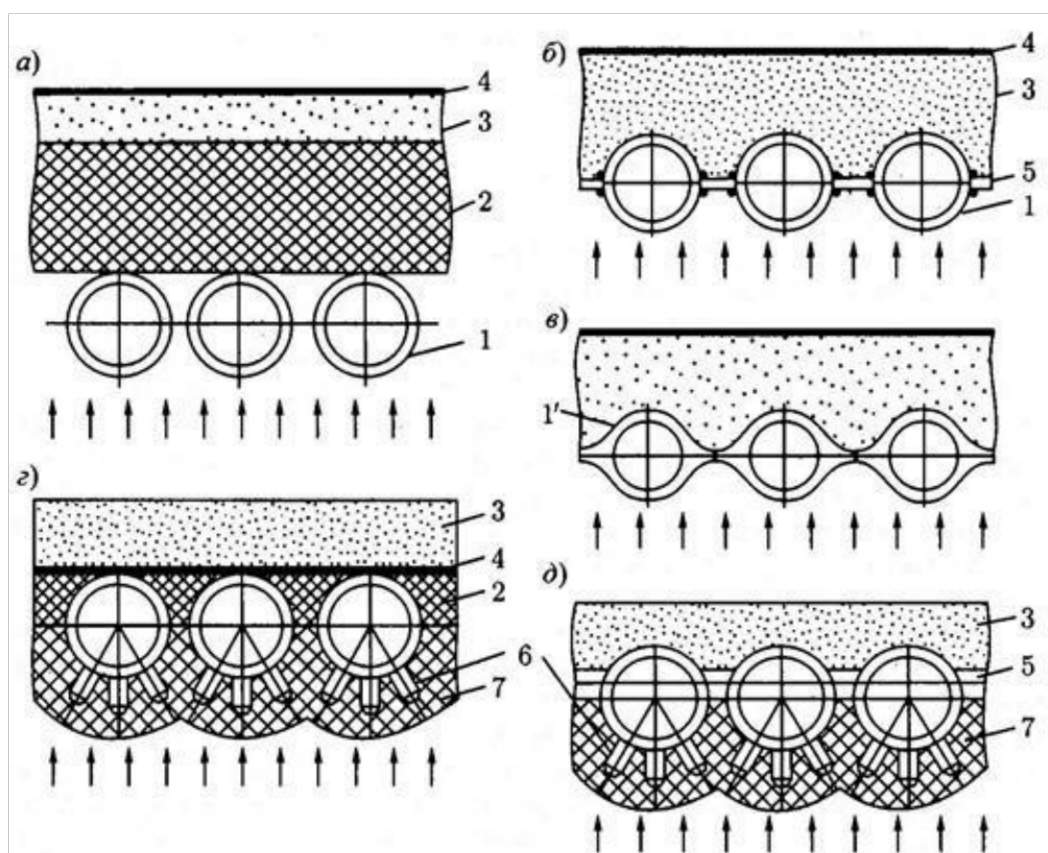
Типы экранирования топки: а — гладкотрубный экран; б — то же с сварными проставками (мембранный); в — газоплотный экран из плавниковых труб; г — футерованный гладкотрубный экран; д — футерованный мембранный экран; 1 — труба; 1' — плавниковая труба; 2 — огнеупорный бетон; 3 — тепловая изоляция; 4 — уплотнительный слой (обмазка, металлический лист); 5 — металлическая проставка; 6 — приварные шипы; 7 — огнеупорная масса.
